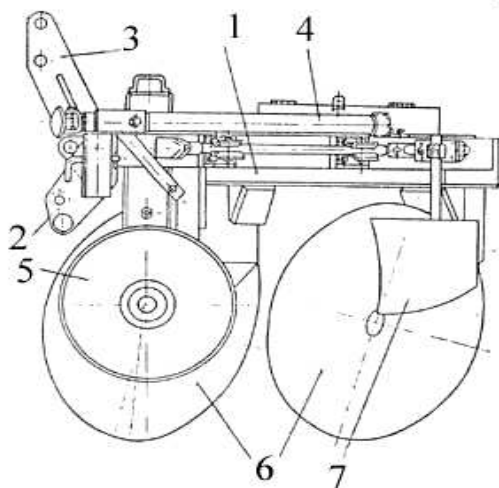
Плуг ПДП-1,2: 1 – рама; 2 – проушина; 3 – стойка; 4 – аутригер; 5 – опорное колесо; 6 – сферический диск; 7 – чистик
